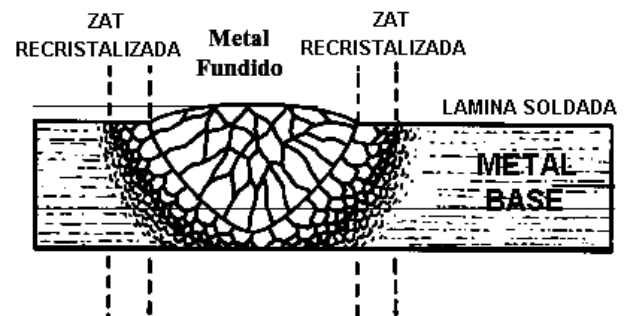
Esquema de las zonas involucradas en un cordón de soldadura [15].
